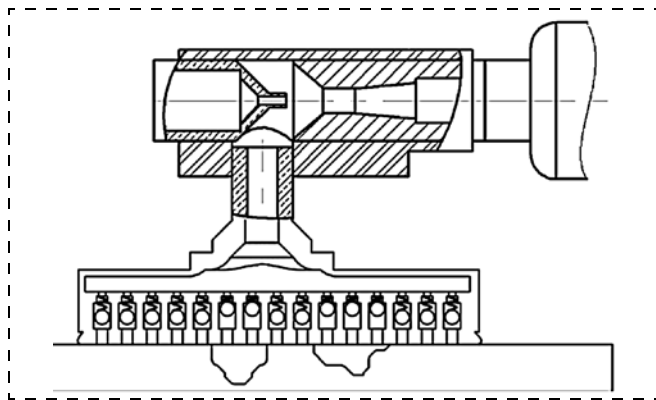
Вакуумное захватное устройство с миниатюрными запорными клапанами
